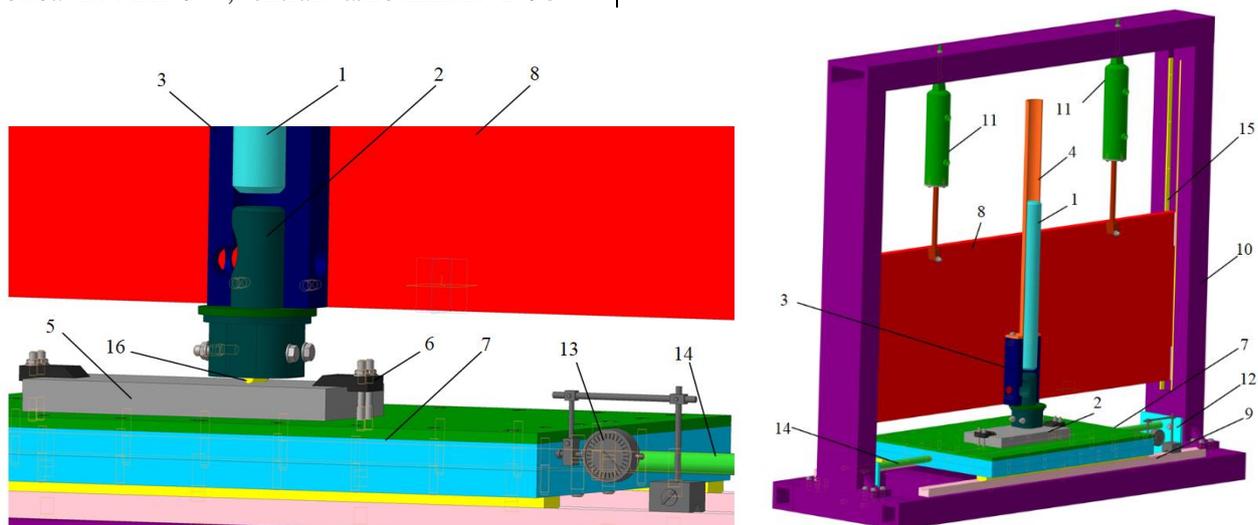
Схема экспериментального стенда, где: 1 – бойк, 2 – волновод, 3 – корпус, 4 – трубчатые направляющие, 5 – обрабатываемая поверхность, 6 – прихваты, 7 – стол, 8 – плита, 9 – поперечная направляющая, 10 – порталная рама, 11 – гидроцилиндры, 12 – упор, 13 – индикатор, 14 – ходовой винт, 15 – направляющие, 16 – инструмент [7]
